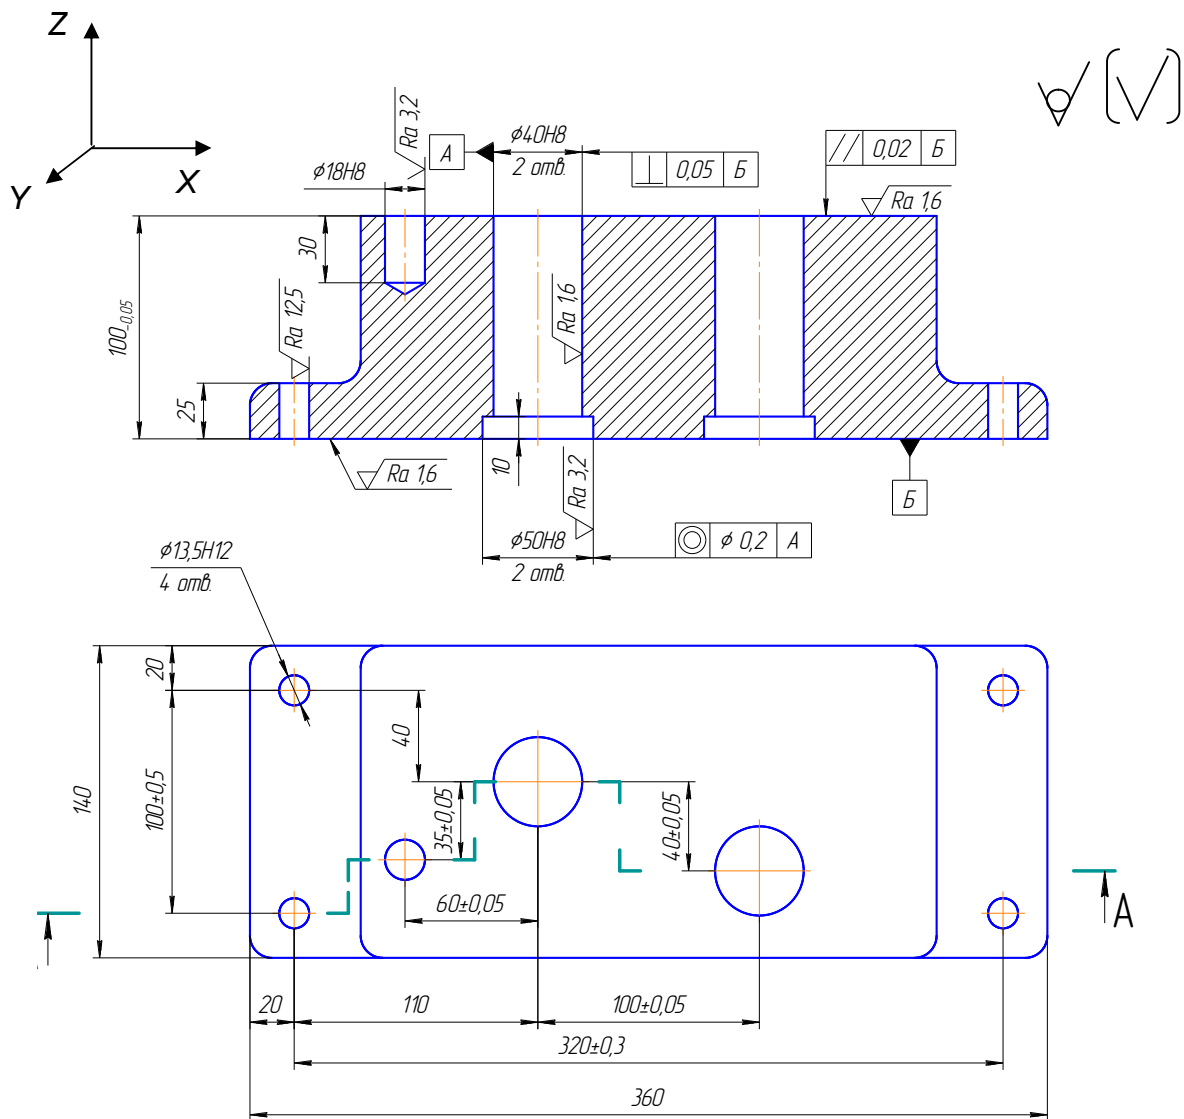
Розташування розмірів на кресленні деталі, яка має оброблені та необроблені поверхні (вихідна заготовка — вилівок)
